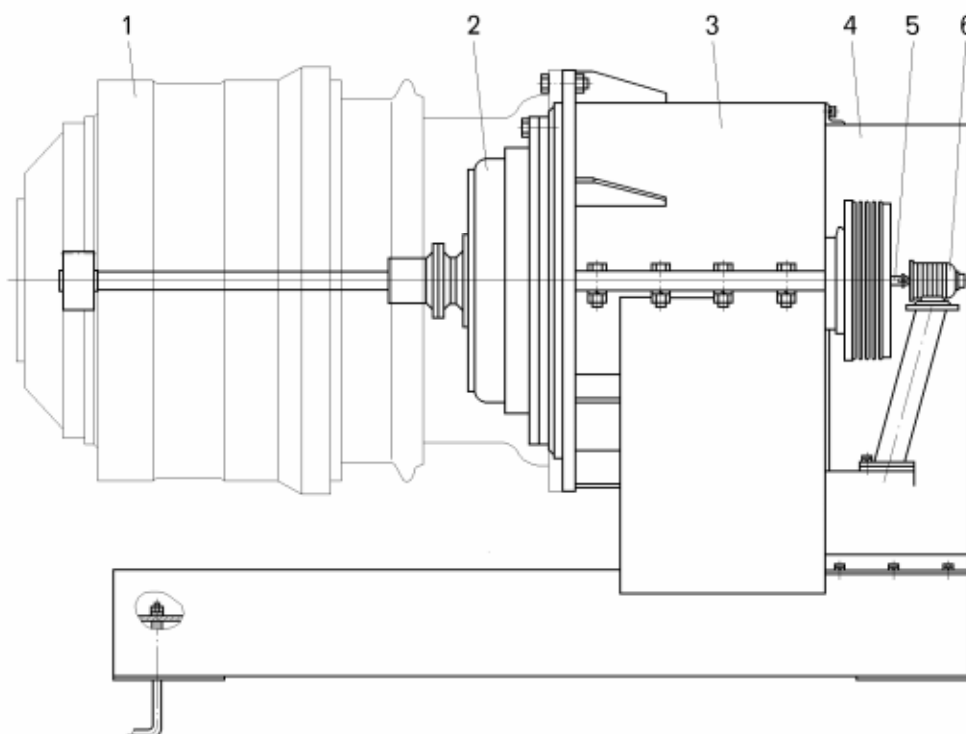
Приспособление для обкатки редуктора электромотор-колеса
